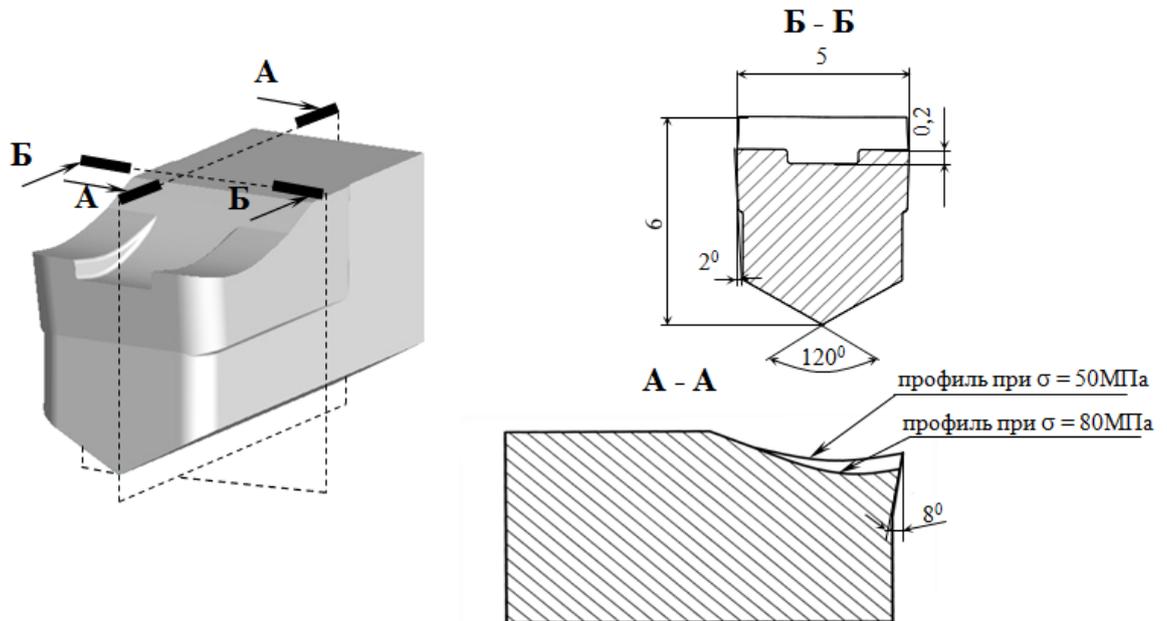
Сменная режущая пластина для отрезных и канавочных резцов, предназначенная для отрезки и прорезки канавок (обрабатываемый материал Сталь 45)
